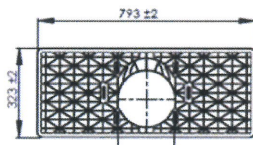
Plaque d'about et plaque d'about ajourée ouverture DN 150 ou DN 200 pour Rigofill inspect
